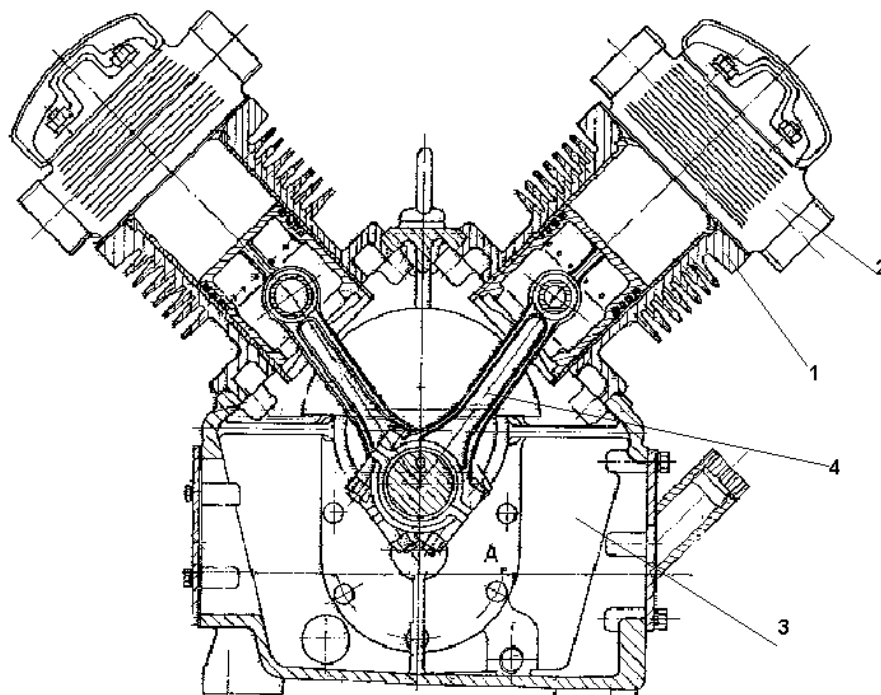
Перерезь главный компрессора V3.7.V Бустер ADP 720
